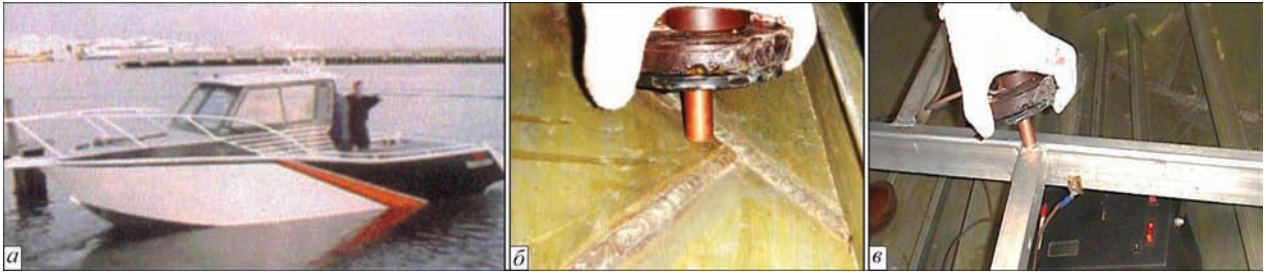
Применение ЭДО при изготовлении корпуса судна из сплава АМгб: а — внешний вид корпуса; б — ЭДО-правка сварных соединений обшивки; в — ЭДО-правка балочных конструкций днища
